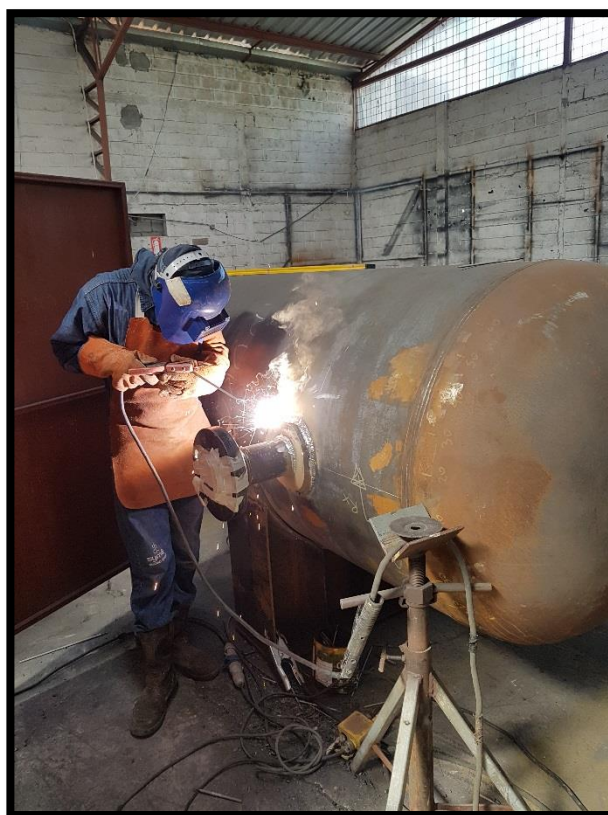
Soldadura de Equipos a Presión
